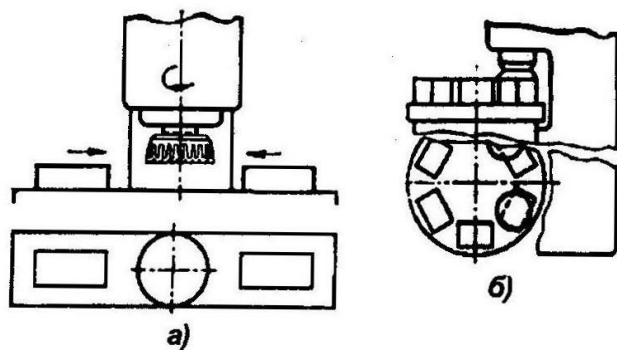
Схеми фрезерування плоских поверхонь фрезами торців методами: а) маятникової подачі; б) безперервної подачі
